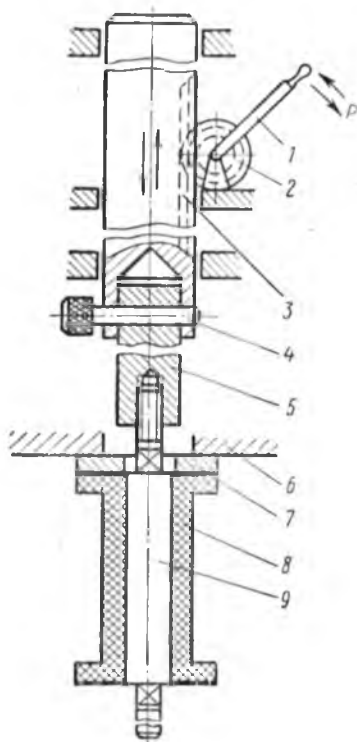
Схема приспособления для извлечения прямолинейных форм:
